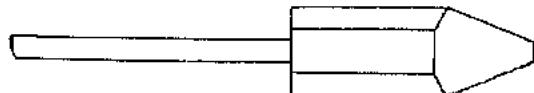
Soldador de punta cuadrada (Electric Materials Co.)
